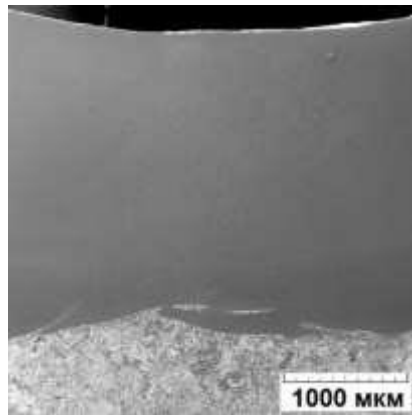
Макрошліф металізаційного покриття після плазмового оплавлення
